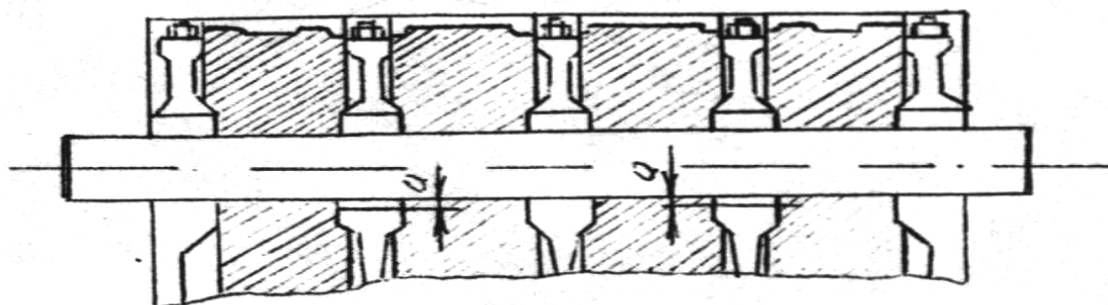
Схема контроля соосности гнезд блока цилиндров под вкладыши коренных подшипников с помощью оправки.
